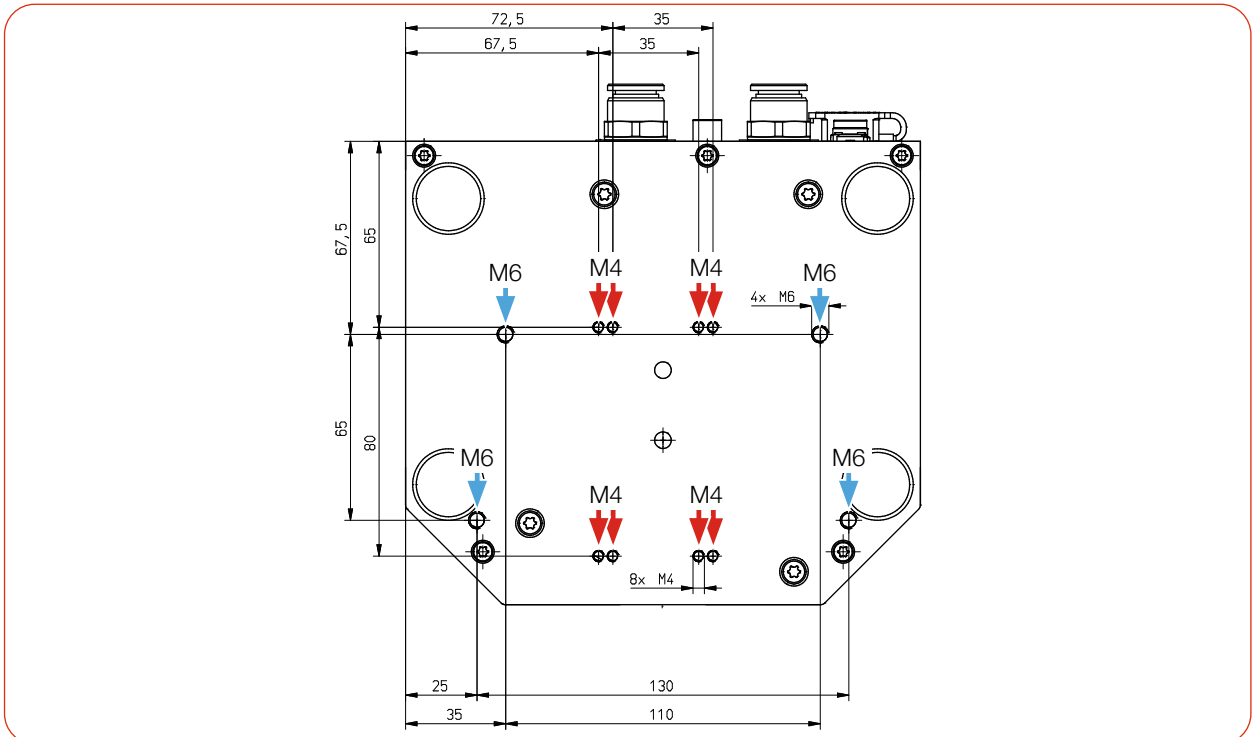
Befestigungsgewinde M4 und M6 im Boden des Gehäuses am CPM+ F-10 (Maße in mm)
